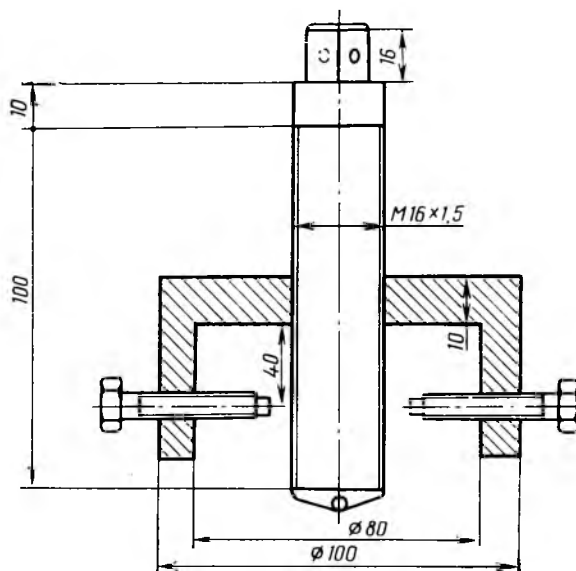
Съемник для разборки и сборки механизма сцепления станка фирмы «Торвегге»
